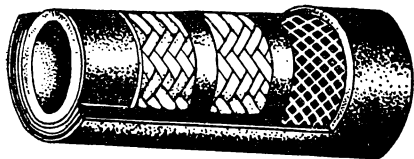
Напорный рукав высокого давления с металлическими оплетками.
